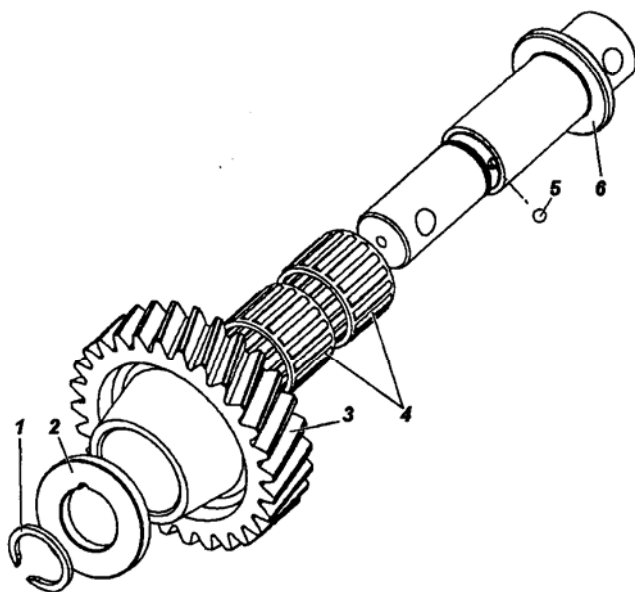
Ось промежуточной шестерни заднего хода: 1 - стопорное кольцо; 2 - упорная шайба; 3 - промежуточная шестерня заднего хода; 4 - игольчатые подшипники; 5 - шарик; 6 - вал промежуточной шестерни заднего хода
